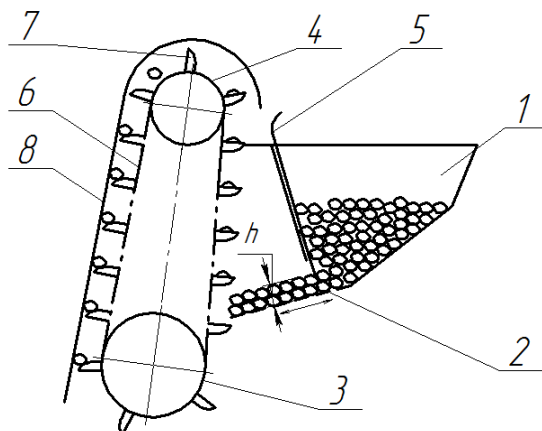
Схема ланцюгово-ложкового висаджувального апарату із коливальною стінкою бункера: 1 – бункер; 2 – коливальний ківш; 3 – ведуча зірочка; 4 – ведена зірочка; 5 – заслінка; 6 – тяговий ланцюг; 7 – ложечка; 8 – кожух
